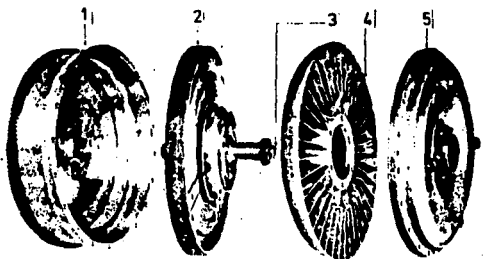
Partes del embrague hidráulico: (1) Tambor del volante (2) Rotor (3) Eje de salida de movimiento de giro (4) Turbina del embrague hidráulico (5) Bomba del embrague hidráulico, que actúa también como ta pa.
